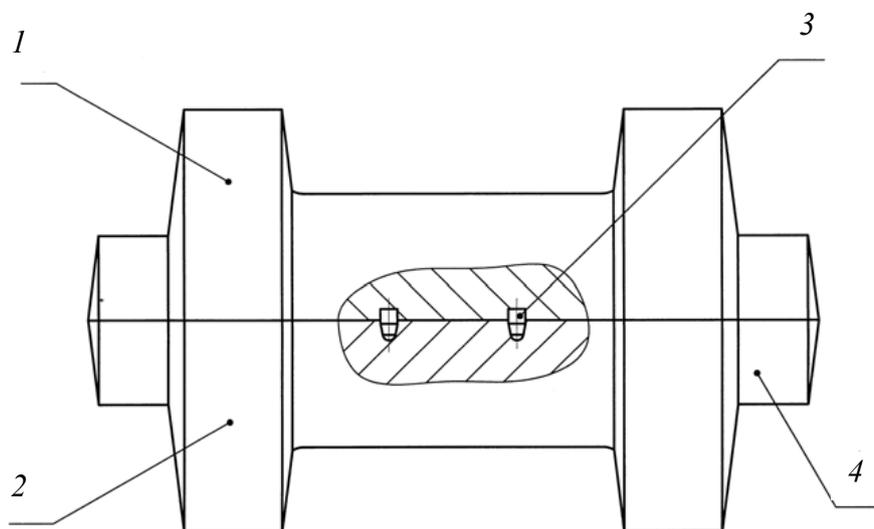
Разъемная литейная модель для отливки «Втулка»:
